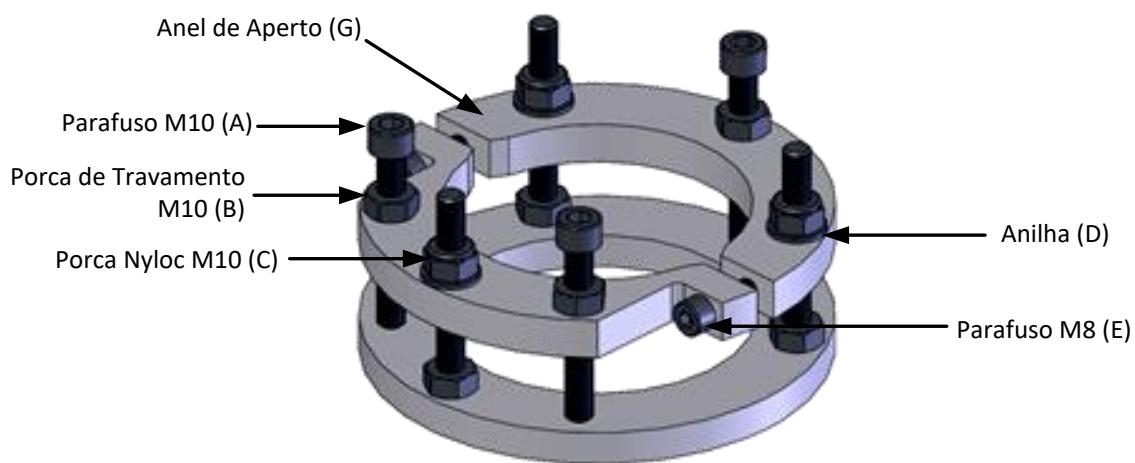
Anel de Aperto Ajustável Montado e Instalado na Placa de Fixação
